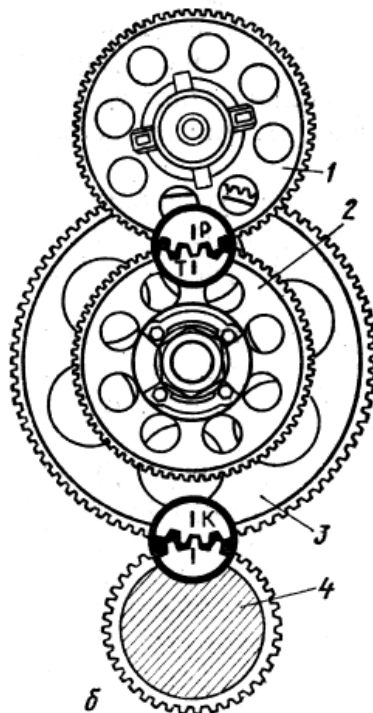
Газораспределительный механизм двигателя СМД-62:
